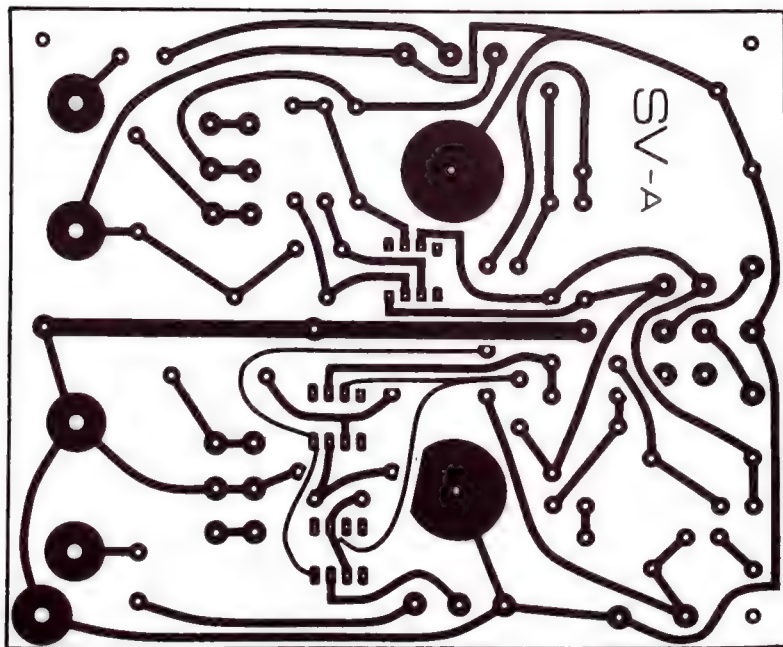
Der Print nimmt nicht nur die Elektronik, sondern auch die meisten mechanischen Bauteile auf.
